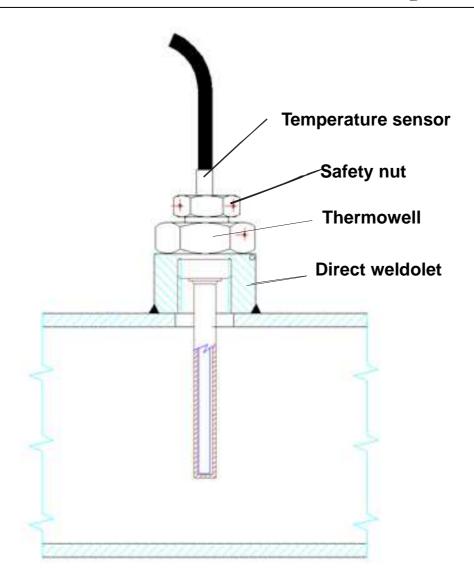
sensore di temperature montato con tasca termometrica diretta
